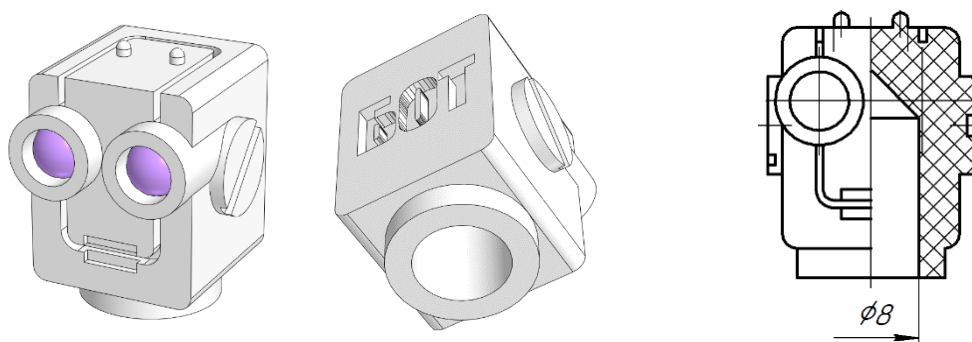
Образец изделия «Колпачок» и его профильный вид с местным разрезом.
